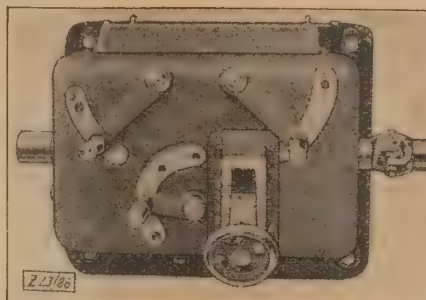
Vorschubröderkasten der Universalfräsmaschine von Biernatzki & Co.
